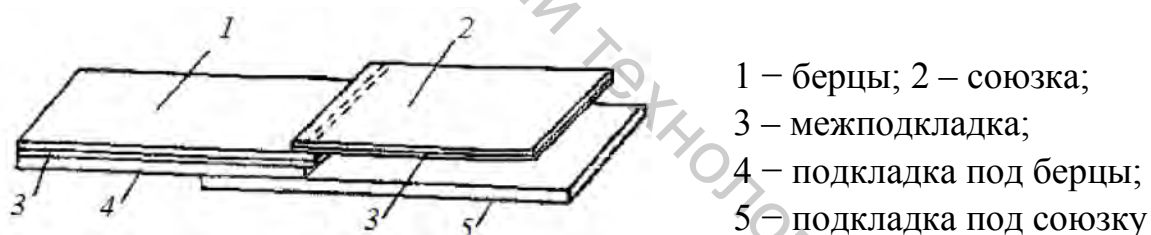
Соединения деталей в заготовке верха обуви
